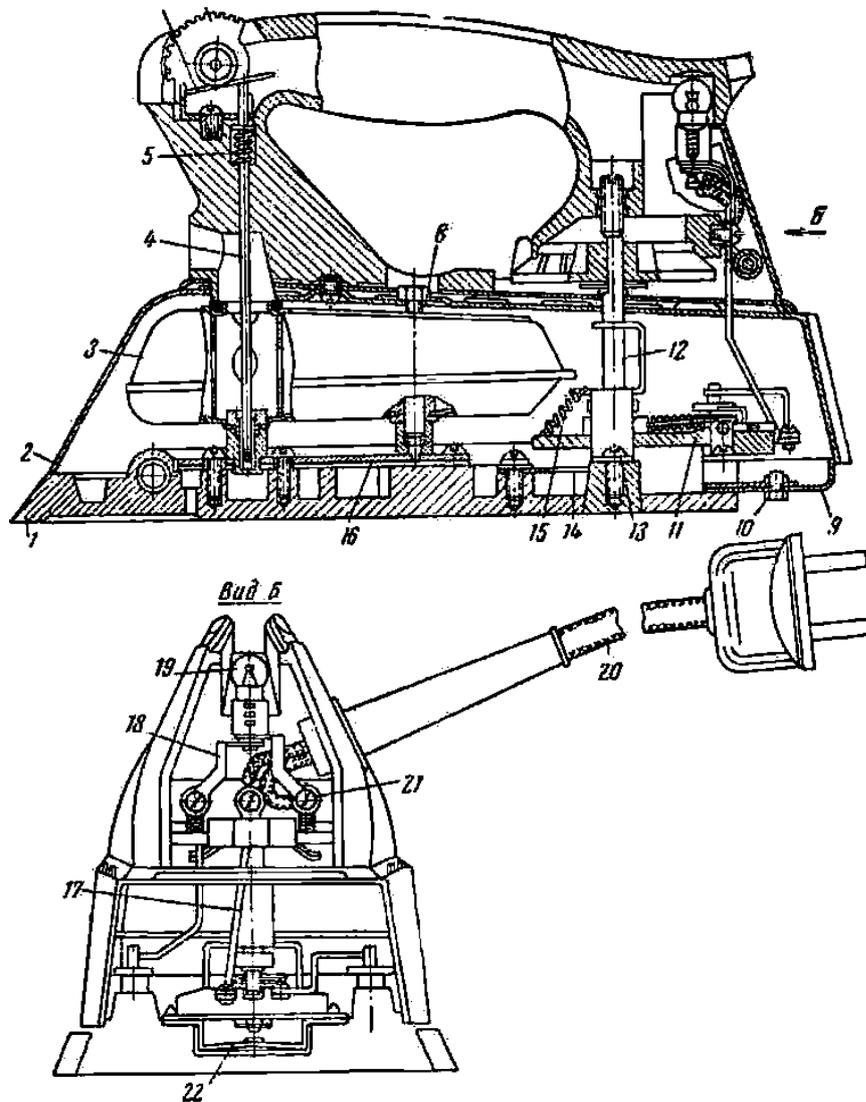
Электрический утюг с терморегулятором и пароувлажителем: 1 — подошва; 2 — кожух; 3 — бачок; 4 — шток рычага пароувлажнителя; 5 15 — пружины; 6 — пластинка; 7 — переключатель; 8 и 10 — винты; 9 — крышка; 11 — терморегулятор; 12 — кулачок; — шайба; 13 — биметаллическая пластинка; 16 — крышка капельницы; 17 — соединительный провод; 18 — шунт сигнальной лампочки; 19 — сигнальная лампочка; 20 — соединительный шпур; 21 — зажимы шнура; 22 — фигурная скоба
